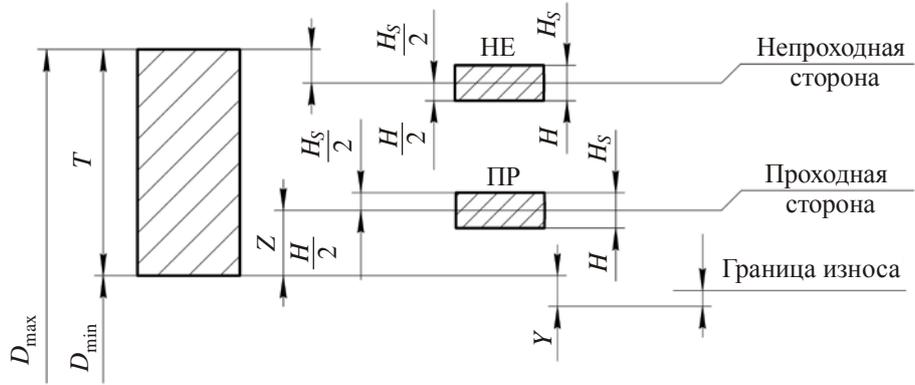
Схемы расположения полей допусков калибров для контроля валов размером до 180 мм:
